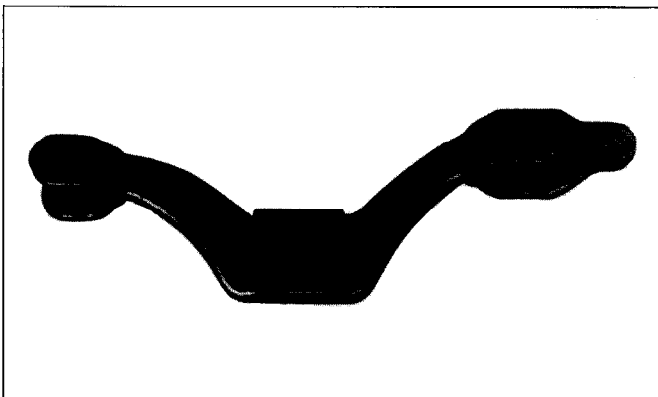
Lichtbogenschweißen mit Elektroden: Spurlenkhebel für Baumaschinen (Stückmasse 17,5 kg, Länge 711 mm) aus 30 Mn 5 V, Schweißquerschnitt: Auge 2 x 700 mm², Gabel 1050 mm²
